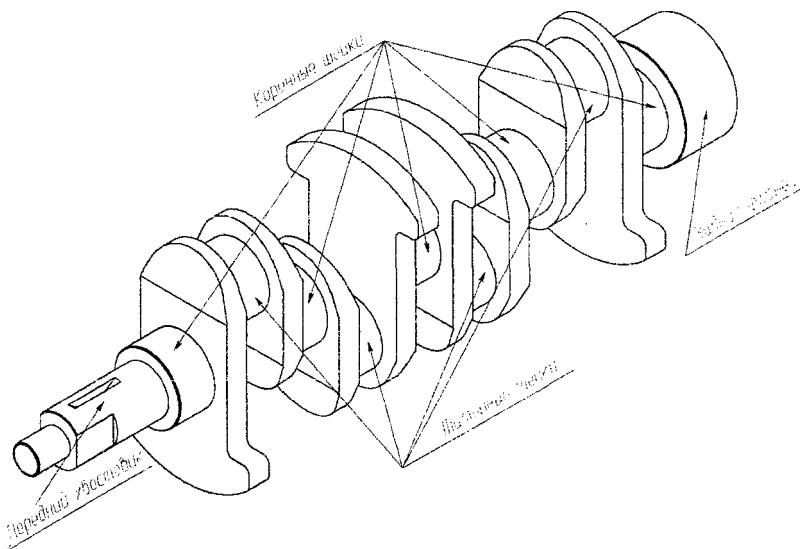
Основные конструктивные элементы коленчатого вала двигателя автомобиля ВАЗ
